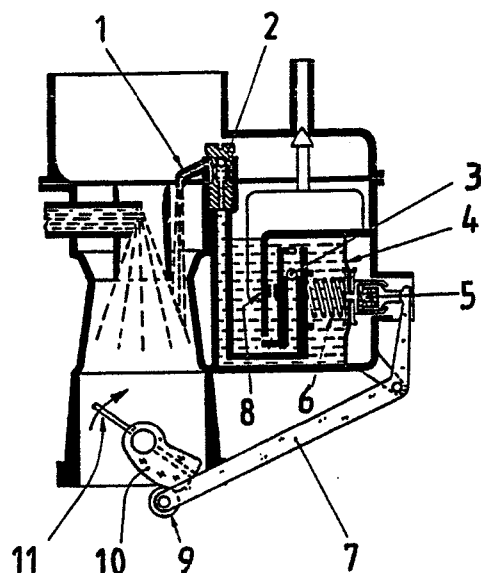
[2] — Carburatore munito di pompa di ripresa a membrana a comando meccanico.
